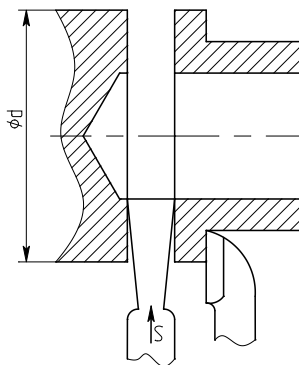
Ескіз оброблення втулки на токарному верстаті
